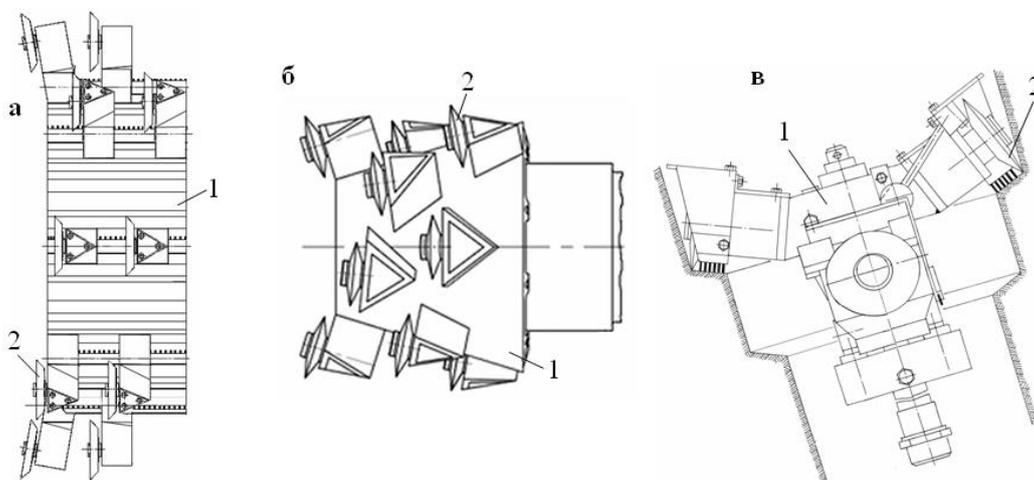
Исполнительные органы с модернизированными узлами крепления дискового инструмента на многогранных призмах: а – шнек; б – коронка; в – расширитель; 1 – корпус; 2 – дисковый инструмент
